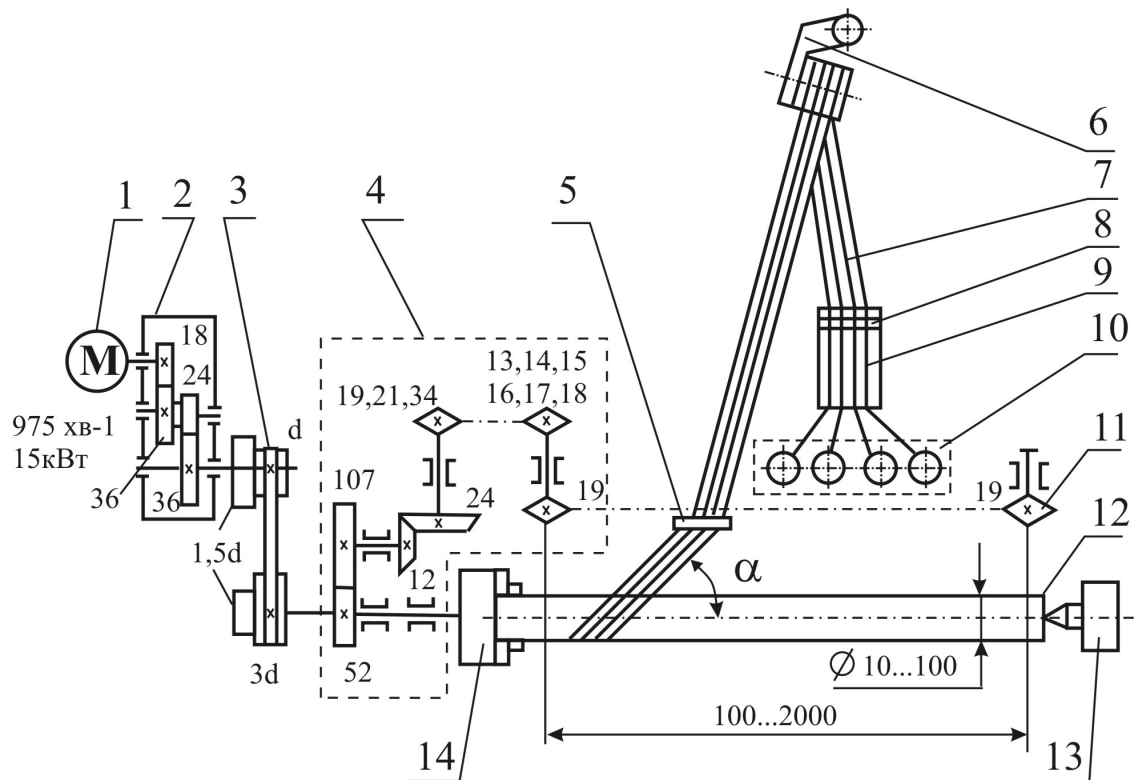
Принципова схема установки для намотування труб з ПКМ
